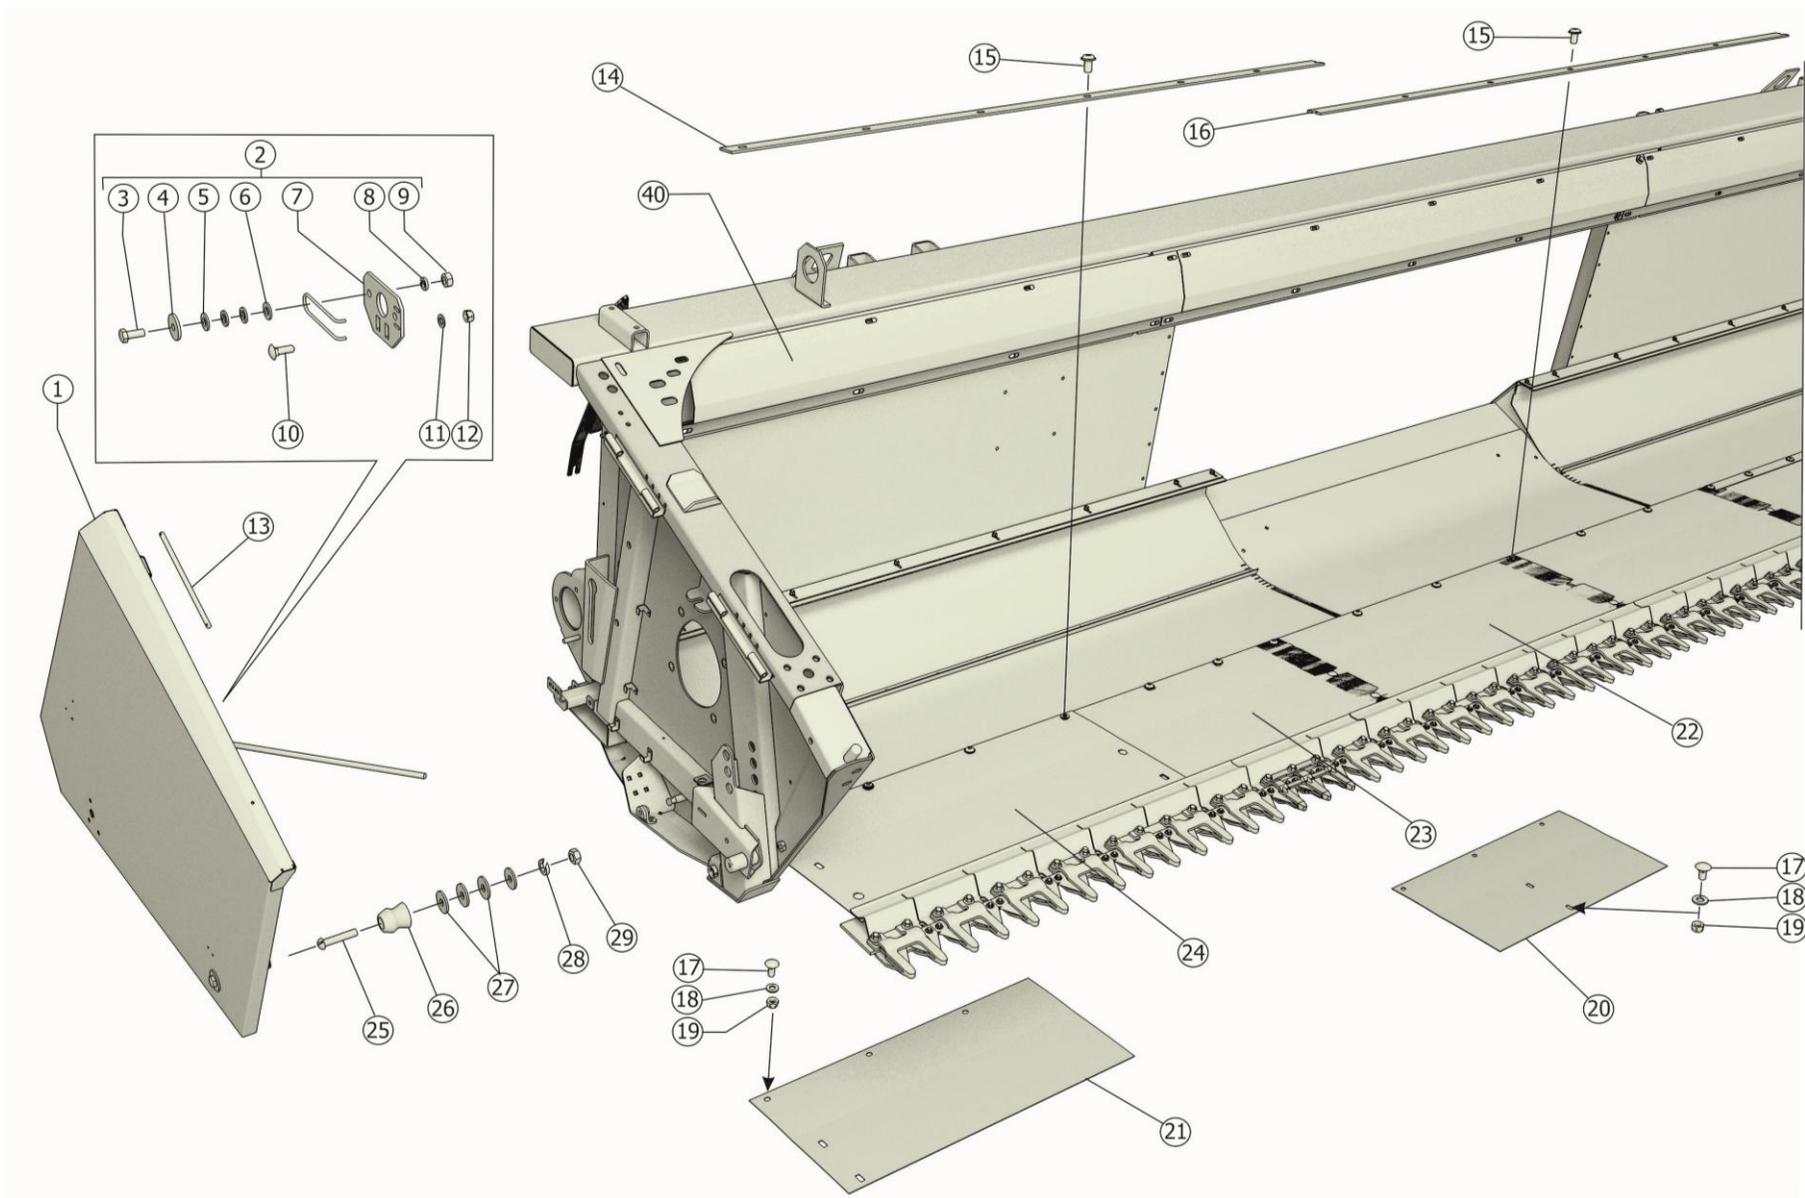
Установка щитов ЖСУ-500.11.00.000Б
